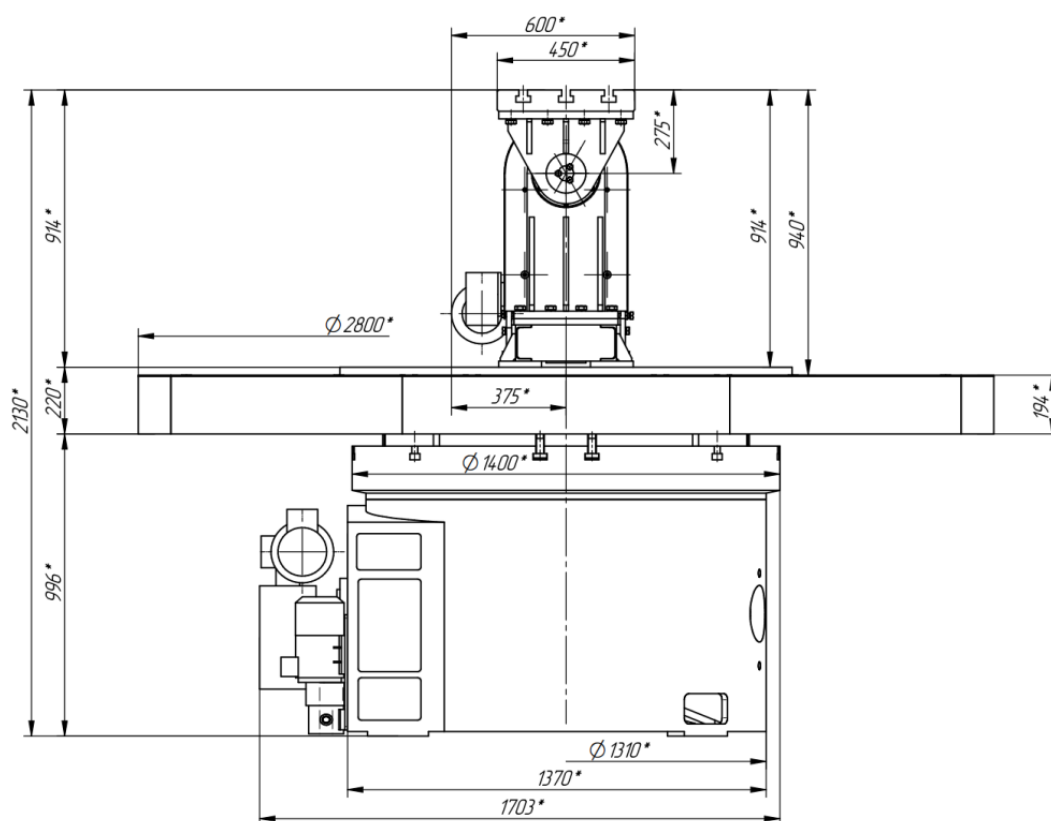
Фрагмент сборочного чертежа 9593-00-00-00СБ
